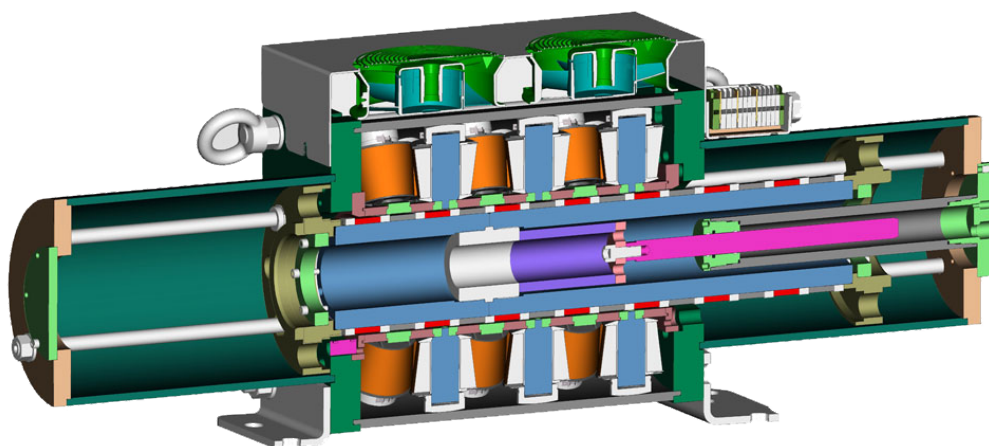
Prinzipieller Aufbau des Linearmotors [21]
